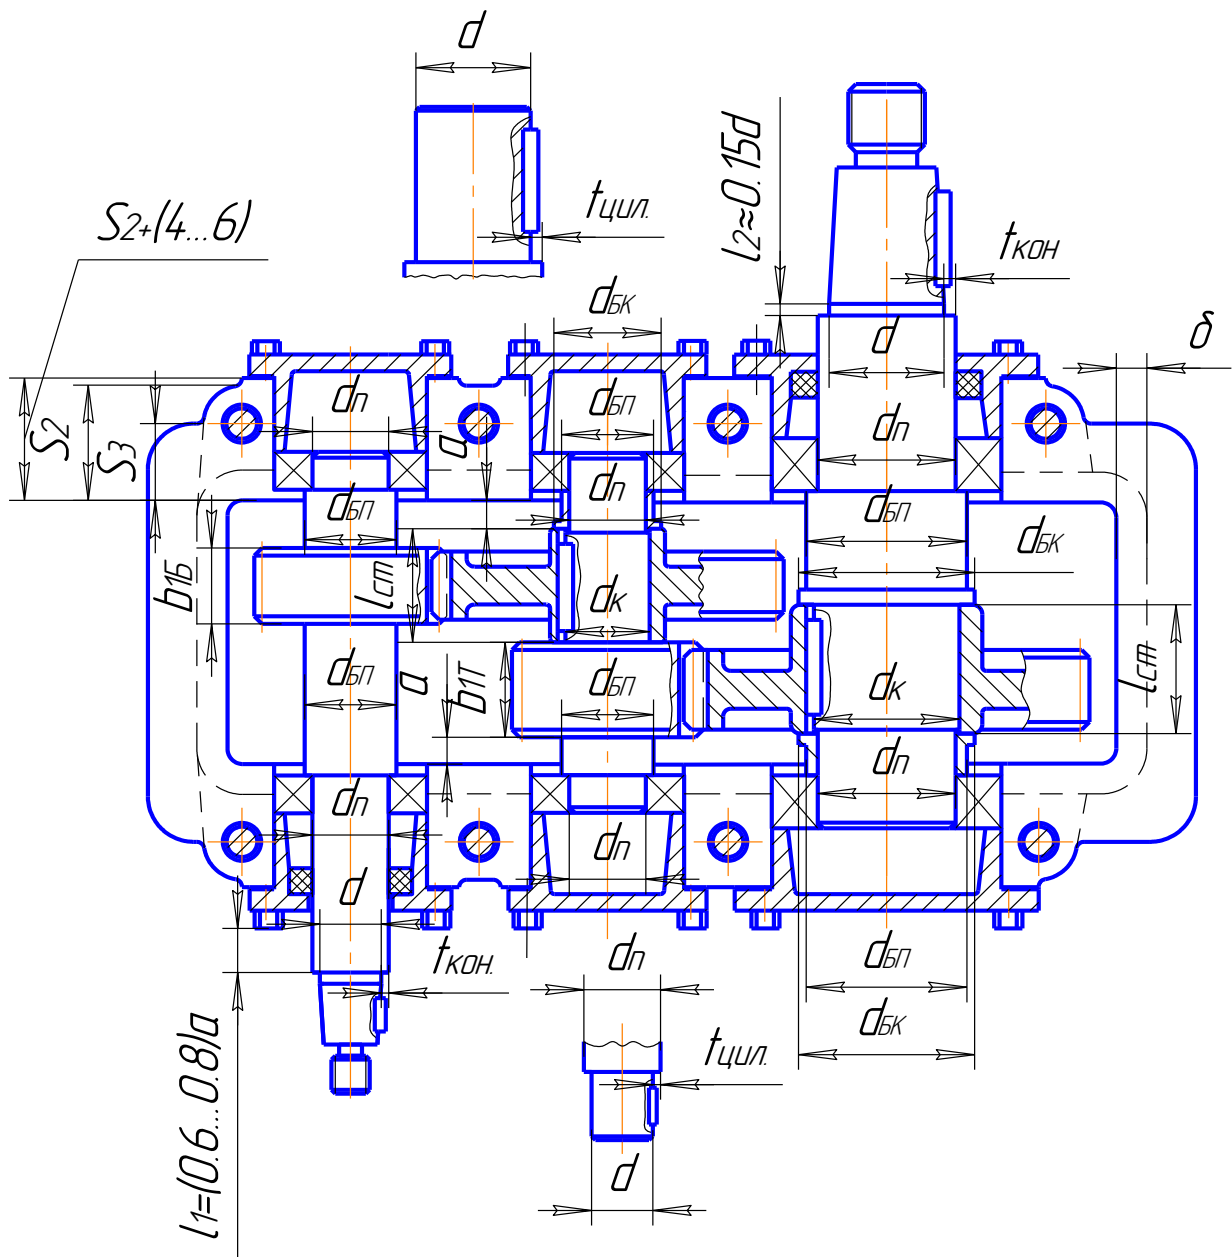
Компоновка цилиндрического двухступенчатого редуктора развернутой схемы с наружным расположением подшипниковых бобышек
